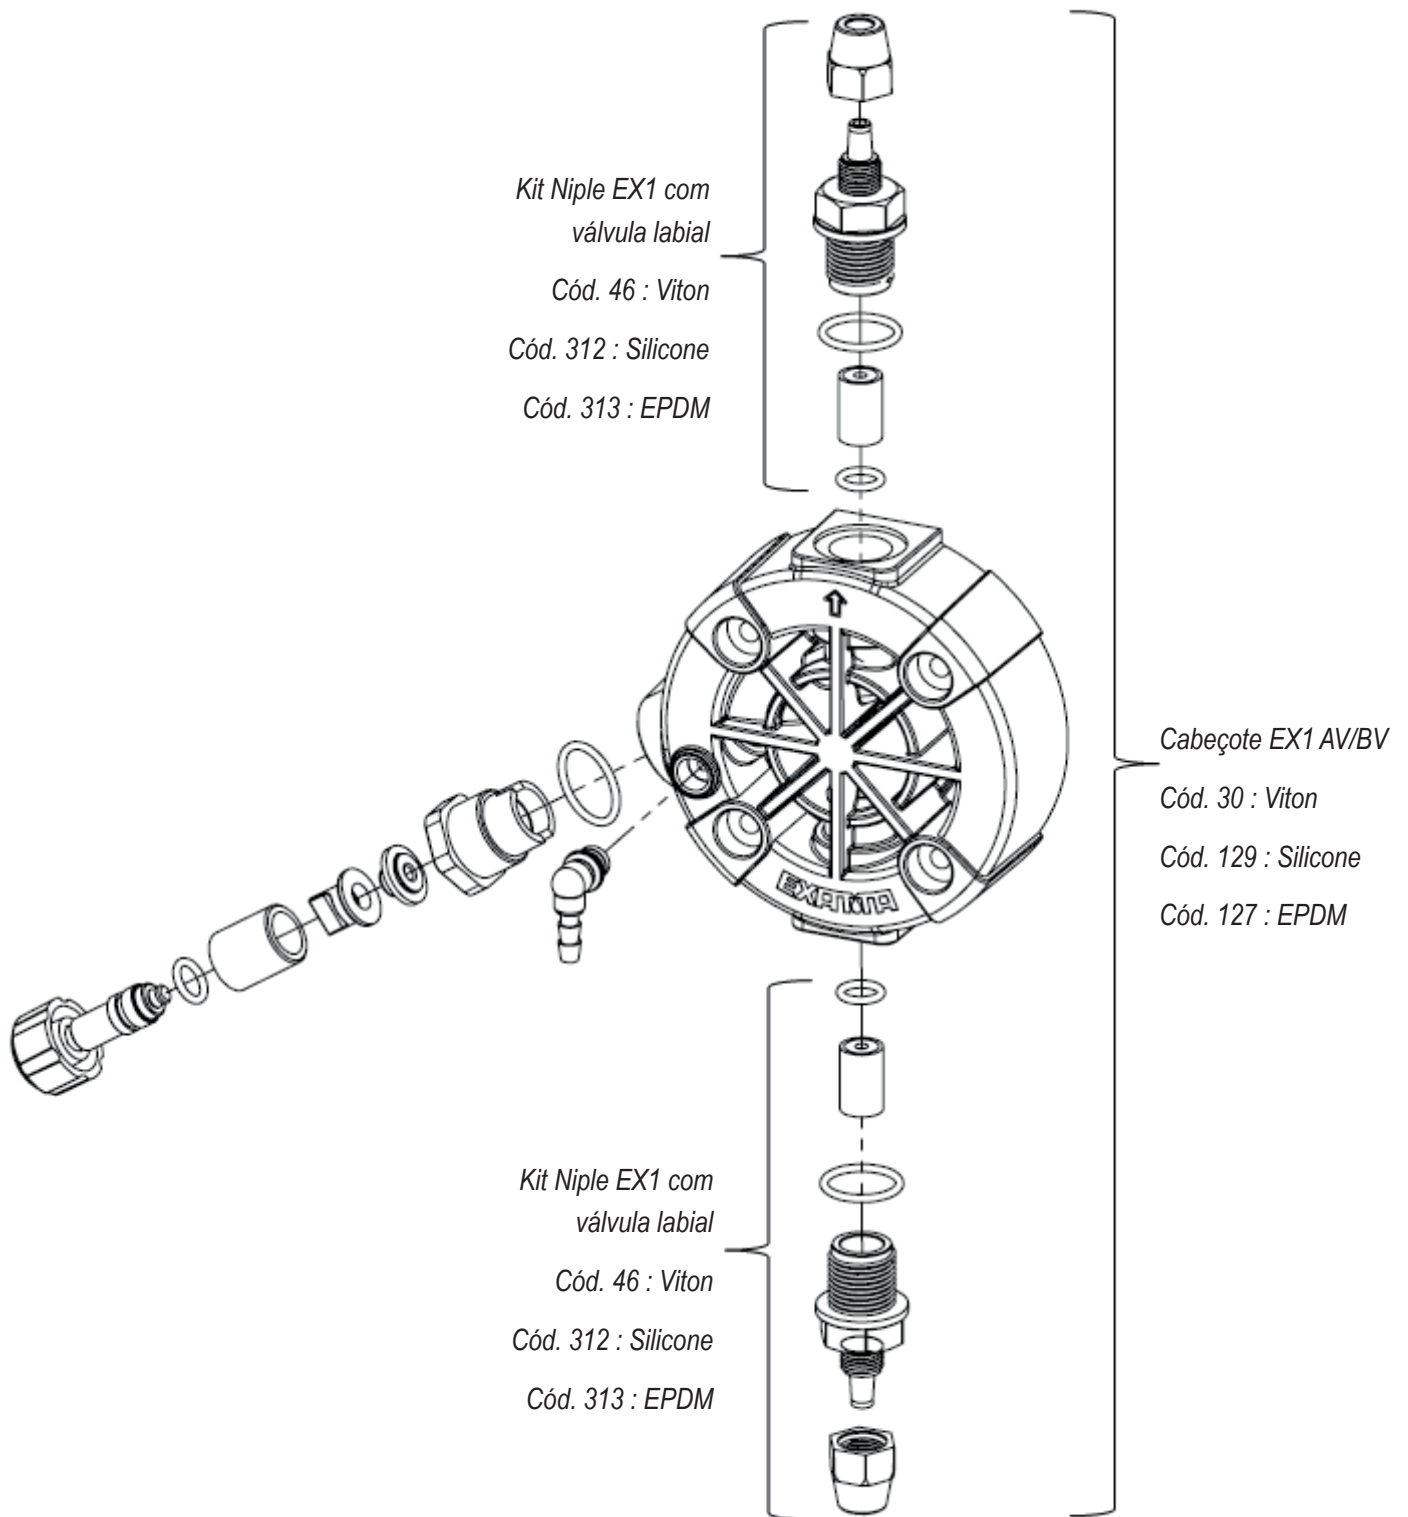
Vista explodida cabeçote EX1 (Válvula Esférica)
